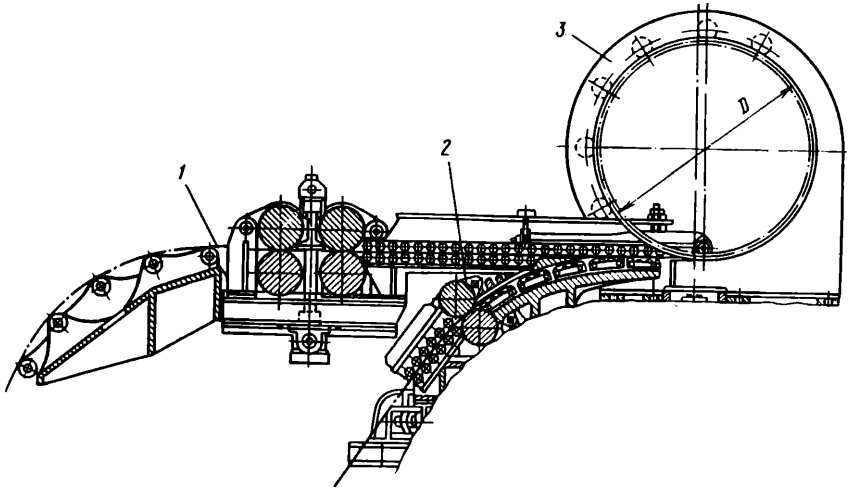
Схема стана для изготовления двухслойных спиральношовных труб:
